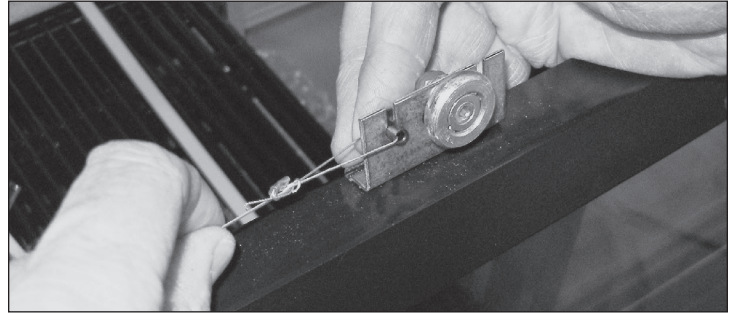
Retire el cable de la puerta del soporte de las ruedecillas.
